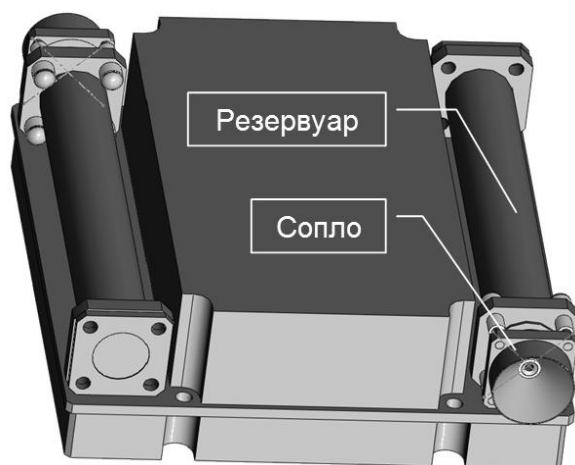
Общая компоновка ионно-плазменного двигателя с жидкометаллическим рабочим телом
